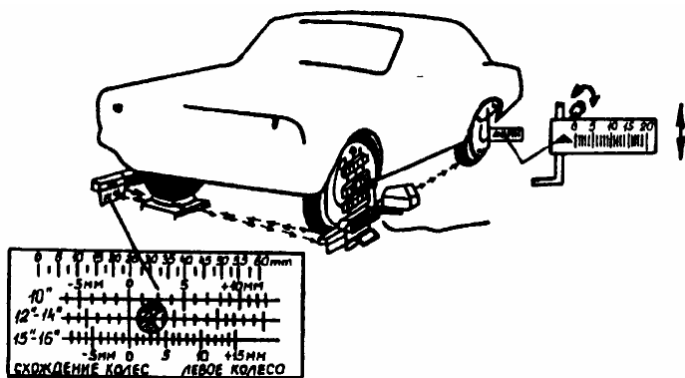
Схема установки приборов при центровке рулевого колеса
